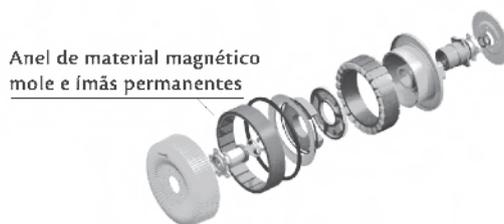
Vista explodida de motor elétrico com uso de ímãs de terras raras³³
